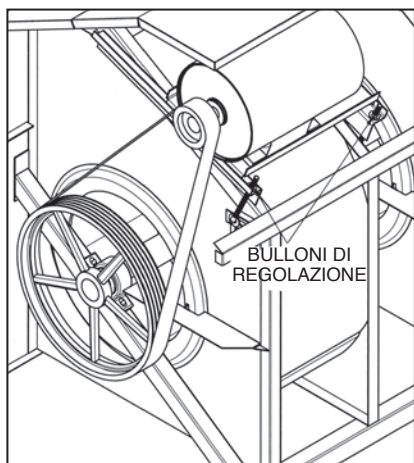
Motore esterno, unità LS, 8X e 3M di grandi dimensioni
